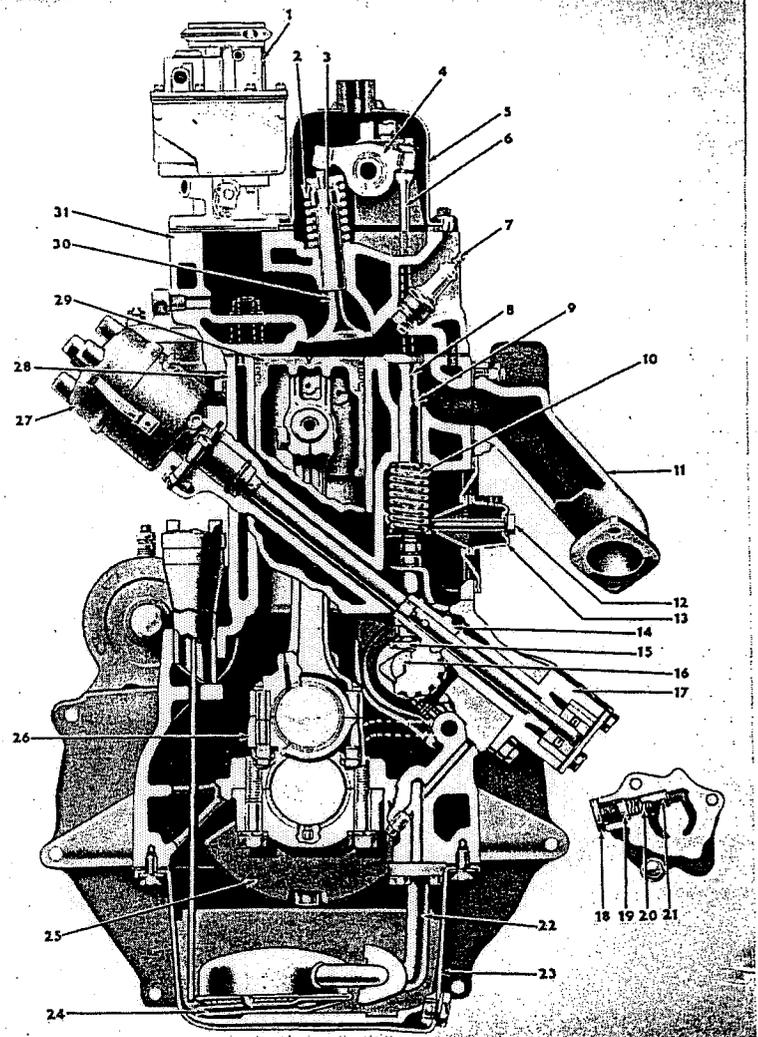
COUPE TRANSVERSALE DU MOTEUR
